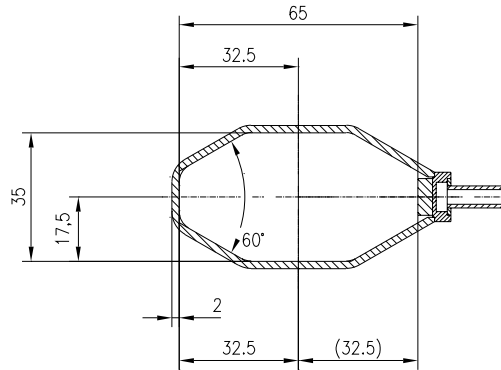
Querschnitt der BESSY II-Vakuumkammer, Maße in Millimetern.
